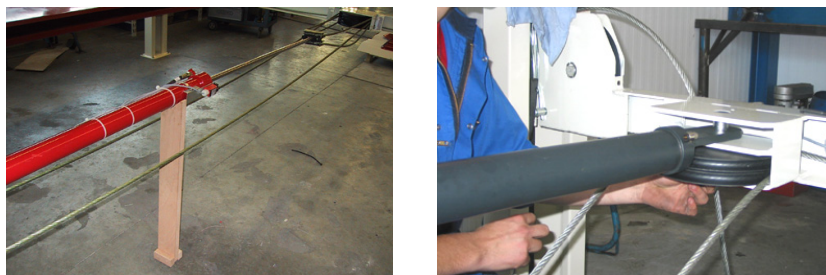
Recorrido de los cables en la barra de acoplamiento I - II y en las columnas
